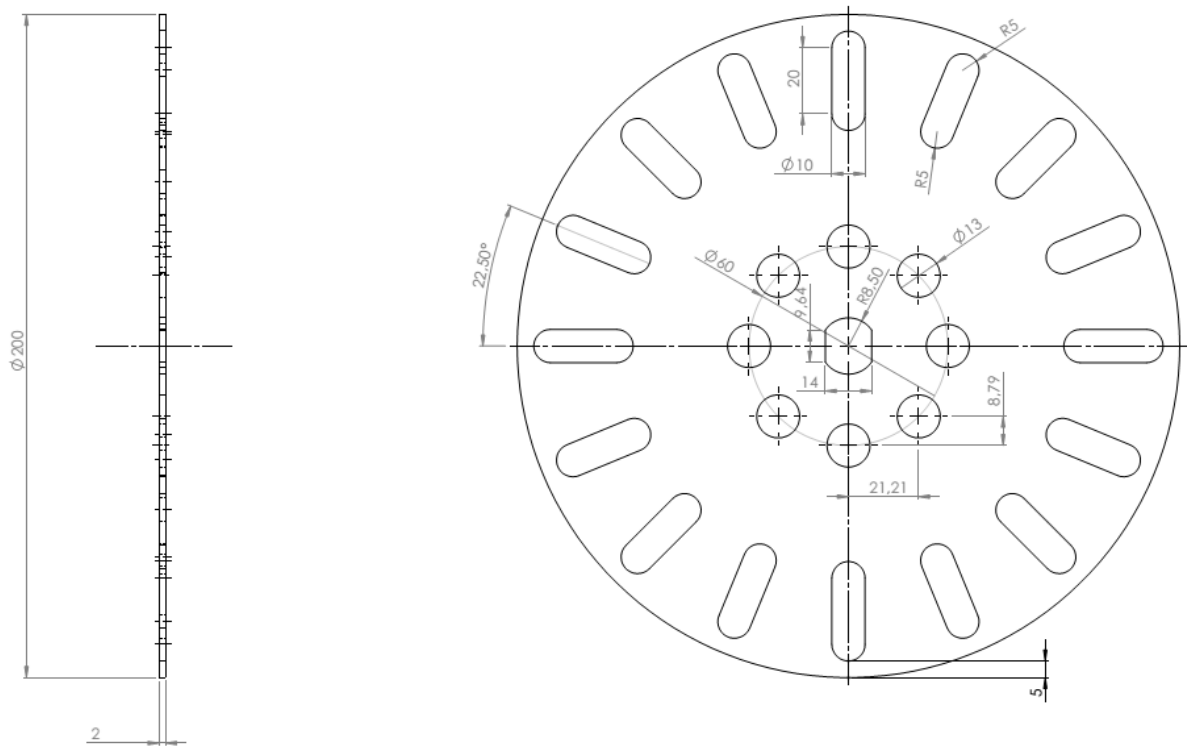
Dimensões (em milímetros) dos discos do rotor tipo D.
